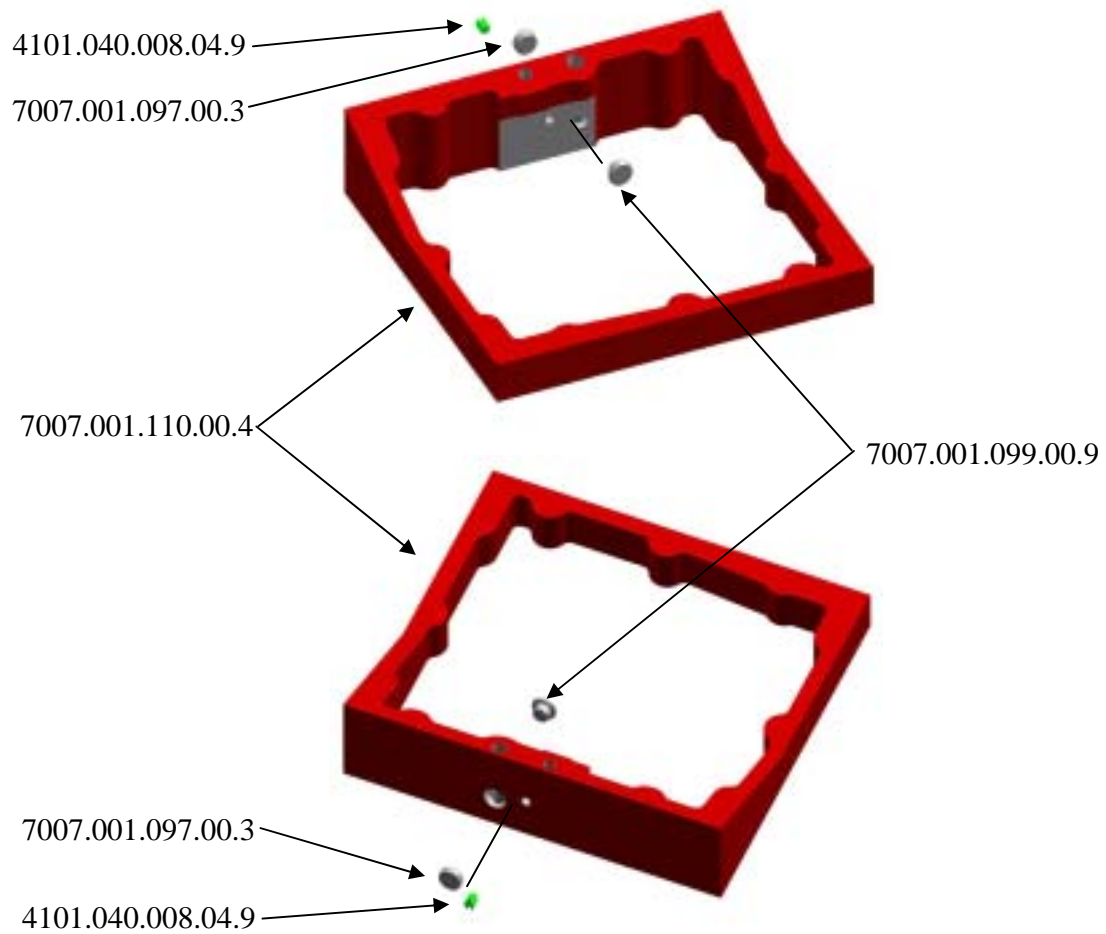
MONTAGEM TAMPÕES CARTER FUNDIDO
